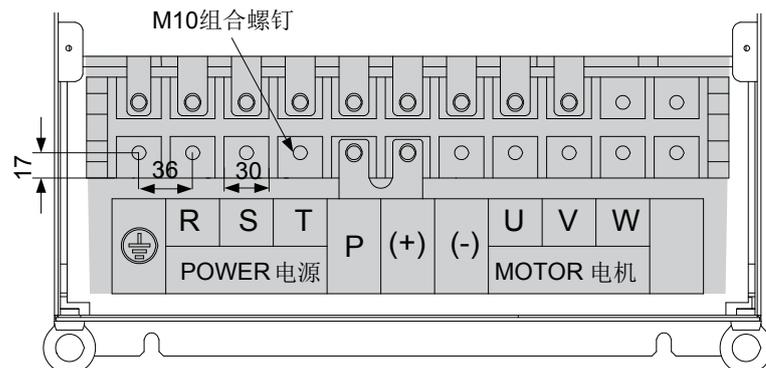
钣金结构 Size G 功率接线端子尺寸图
